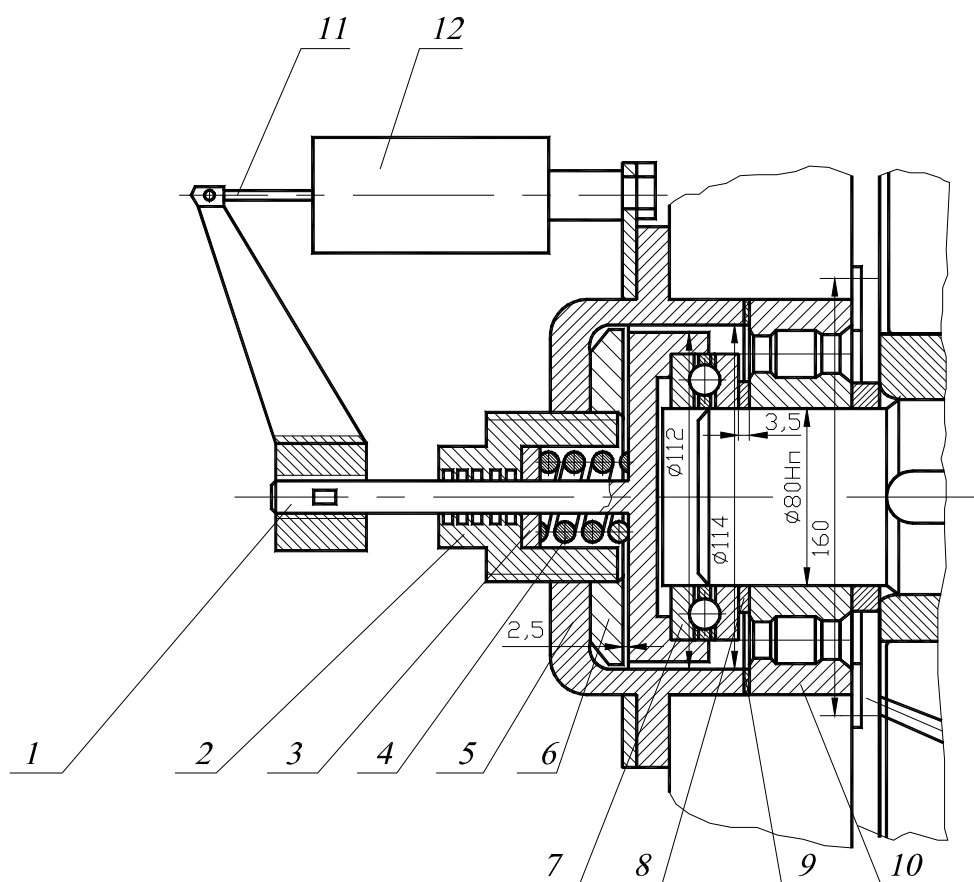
Конструкция модернизированного узла подшипникового узла редуктора ЦДН-40
